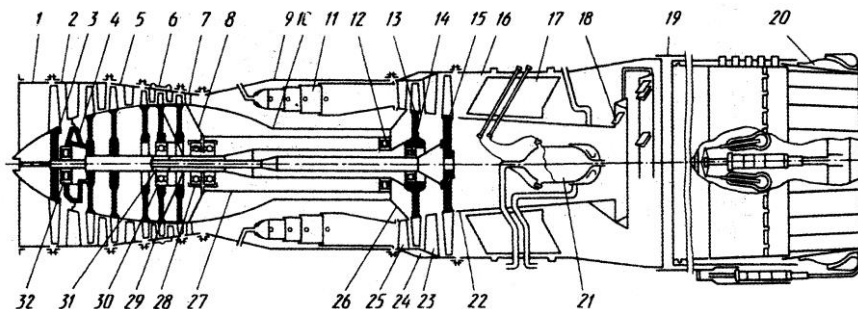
Двухвальный турбореактивный двигатель с форсажной камерой: 1,2,5,6,7 - корпуса компрессора; 4, 8, 26 - корпуса опор; 3, 29 - роторы компрессоров низкого давления КНД и компрессоров высокого давления КВД; 9 - наружный корпус камеры сгорания; 10 - внутренний корпус камеры сгорания; 11 - жаровая труба камеры сгорания; 12, 14 - опоры роторов турбин низкого давления ТНД и турбин высокого давления ТВД; 13, 15 - роторы ТНД и ТВД; 16, 22 - наружная и внутренняя обечайки форсажной камеры; 17 - радиальные стойки; 18 - стабилизаторы; 19 - удлинительная труба; 20 - реактивное сопло; 21 - форкамера; 23, 25 - сопловые аппараты; 24 - корпус газовой турбины; 27 - корпус подшипников; 28, 30, 32 - опоры компрессора; 31 - шлицы
